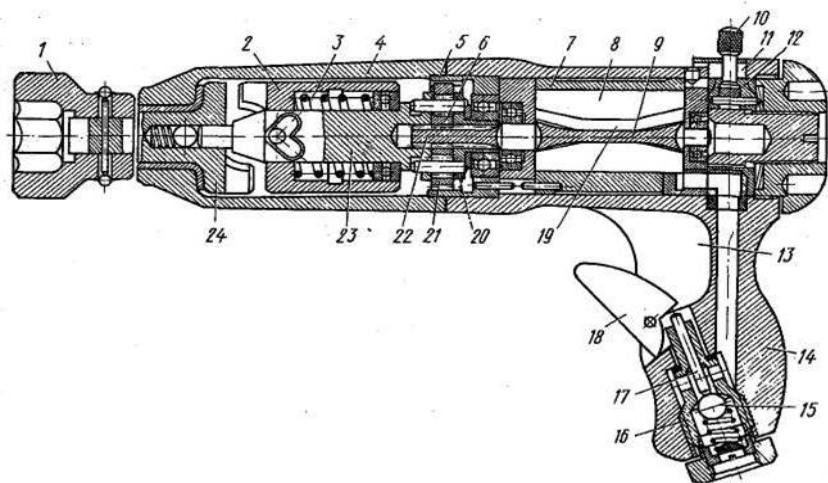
Пневматический реверсивный гайковерт ИПЗ102. Общий вид
